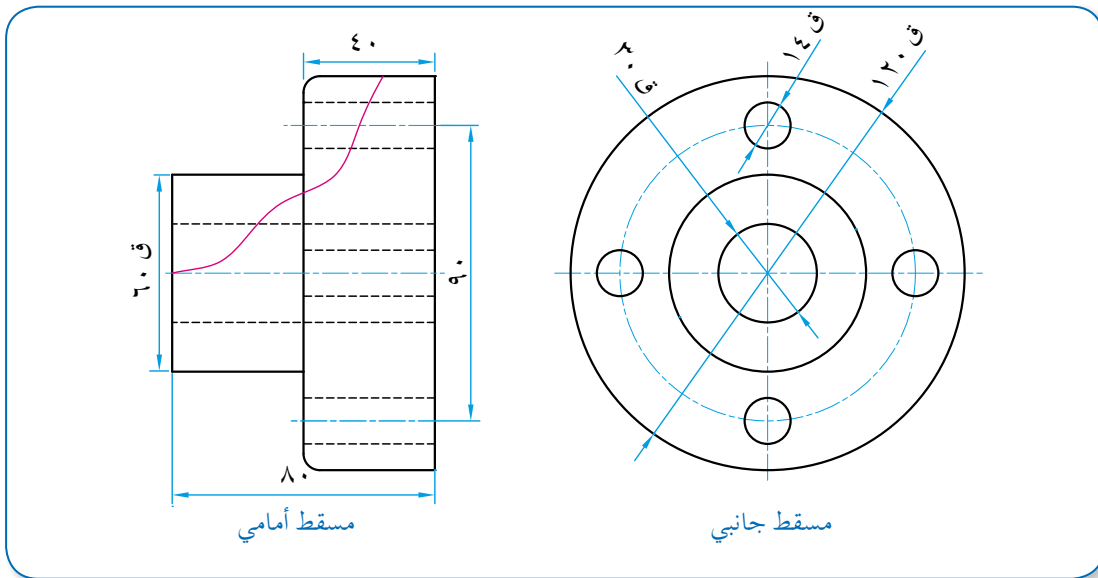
مسقط أمامي ومسقط جانبي لدليل الصمام.
